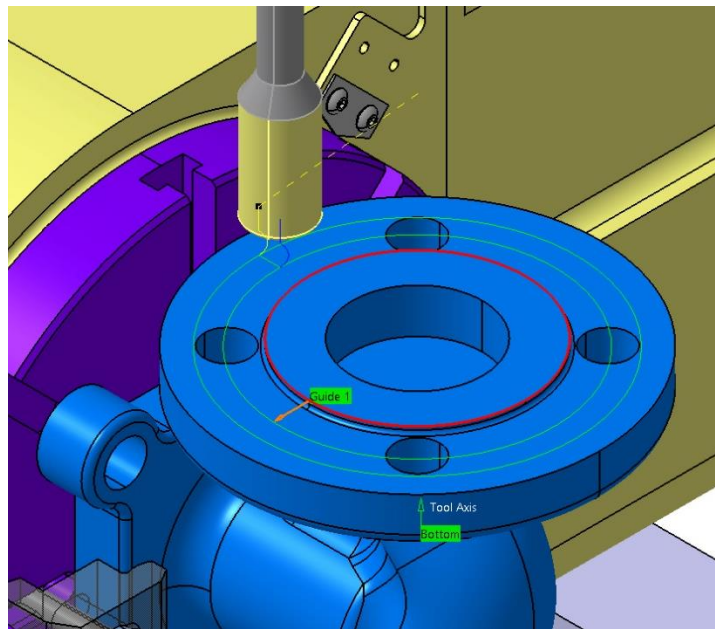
Траекторія руху фрези при обробці уступу торця деталі
